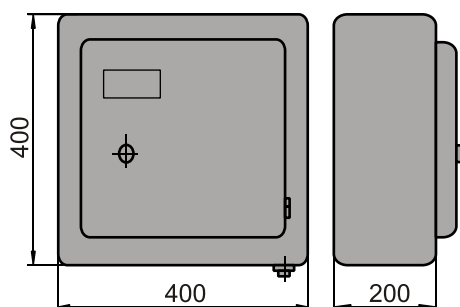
Габаритные размеры щитка ЩИТ-1, ЩИТ-2
